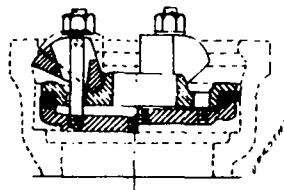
TAMPÃO PARA BOLSA, PATENTEADO (83*)
